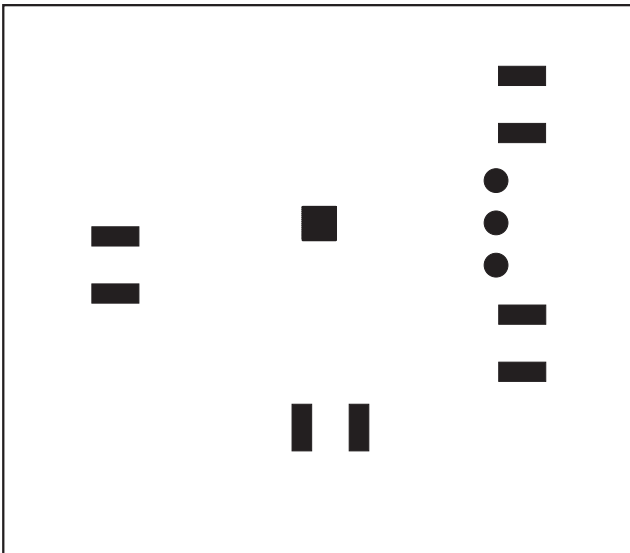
MAX2043评估板PCB布局—底层阻焊层
